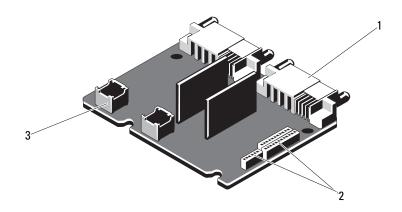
Composants de la carte de montage pour cartes d'extension PCle 1
